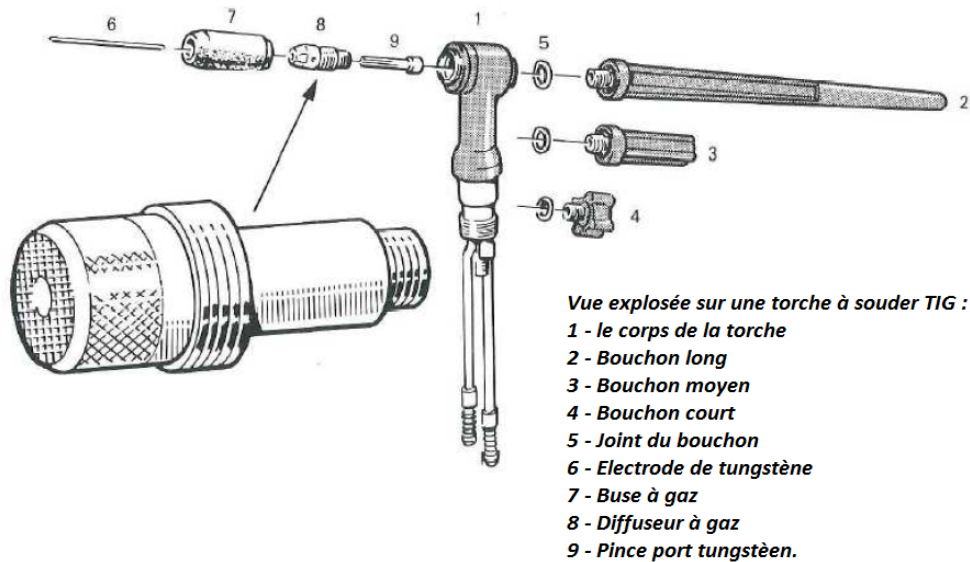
Vue explosée d'une torche à souder TIG [3].
